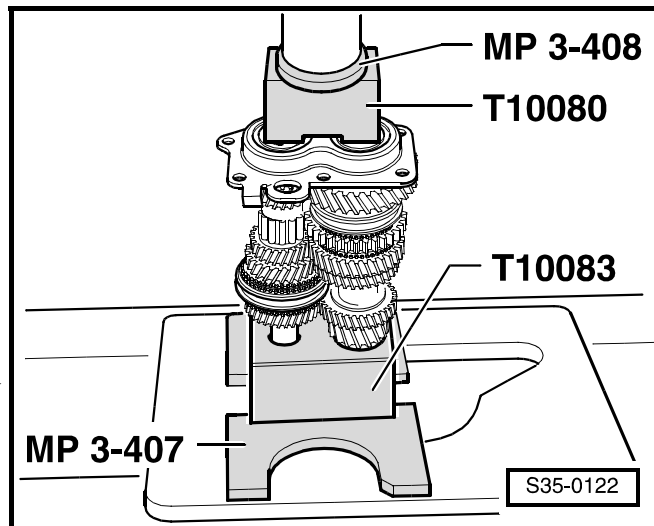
Разборка и сборка скользящей муфты и каретки синхронизатора для 5-ой передачи ►
